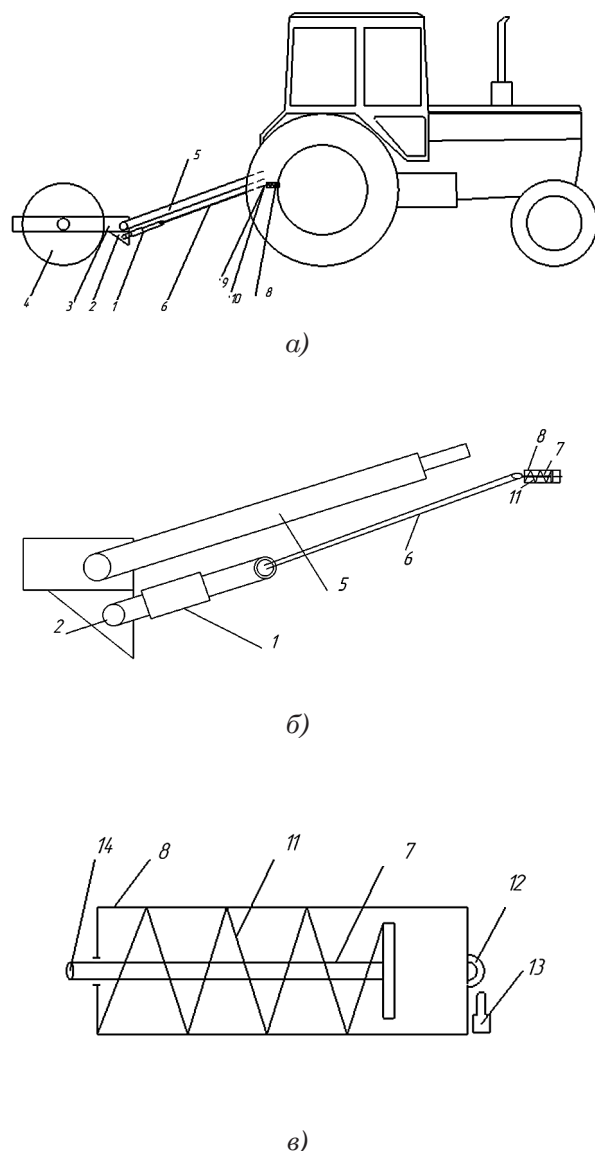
Устройство для автоматической корректировки нагрузки на почвообрабатывающий каток:
